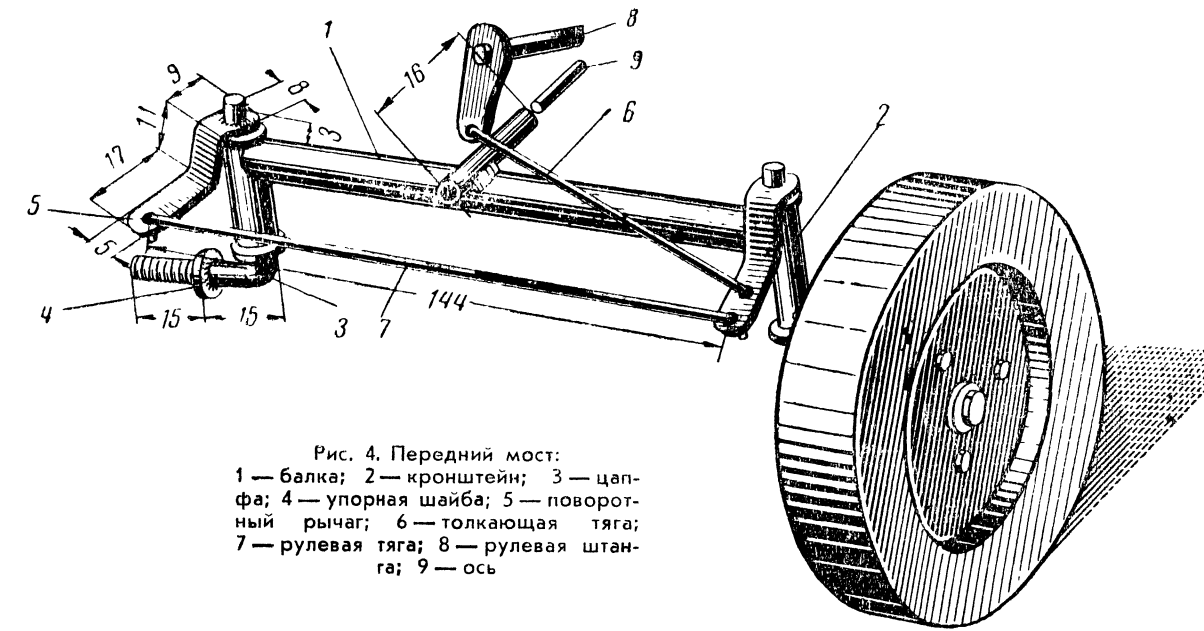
Передний мост: 1—балка; 2—кронштейн; 3—цапфа; 4—упорная шайба; 5—поворотный рычаг; 6—толкающая тяга; 7—рулевая тяга; 8—рулевая штанга; 9—ось
